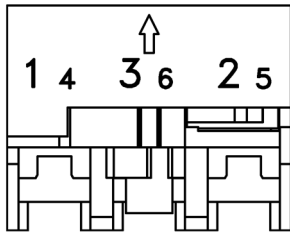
Kennzeichnung der Steckpositionen auf dem 3-fach Halter
